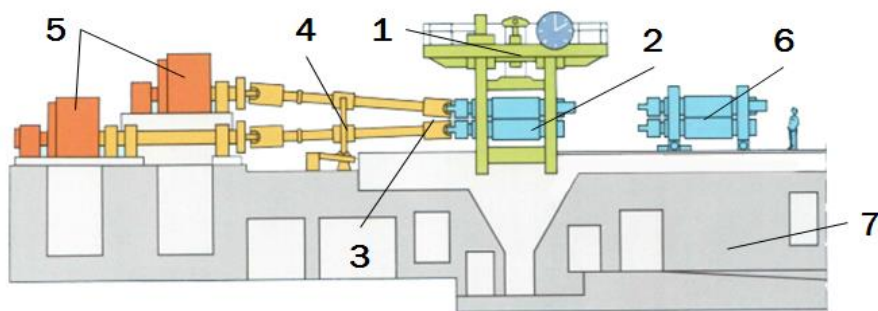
Схема главной линии реверсивной рабочей клетки дуо 1000:
